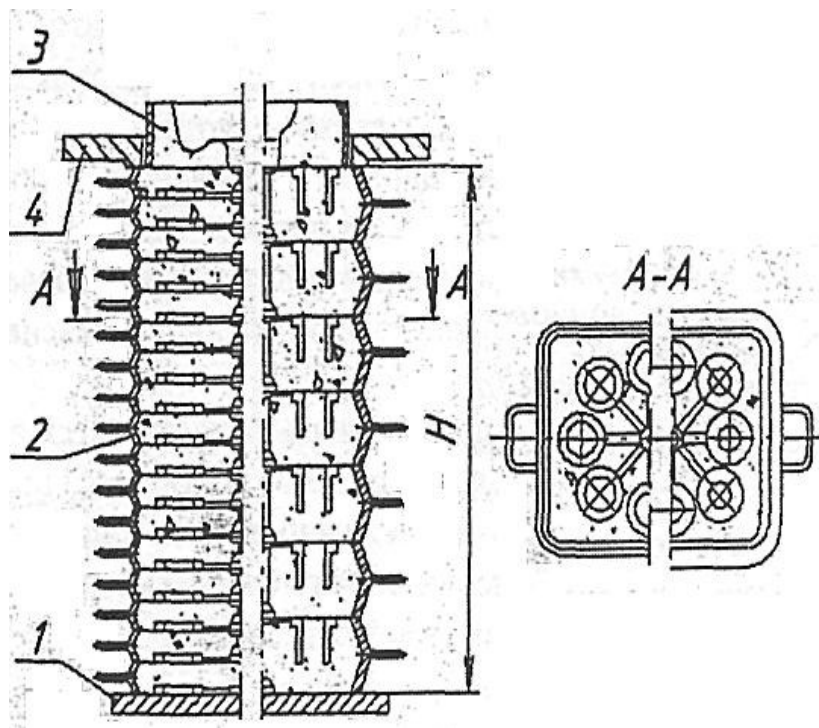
Стопочная формовка. Форма в сборе. 1- поддон ; 2- опока ; 3- груз ;
